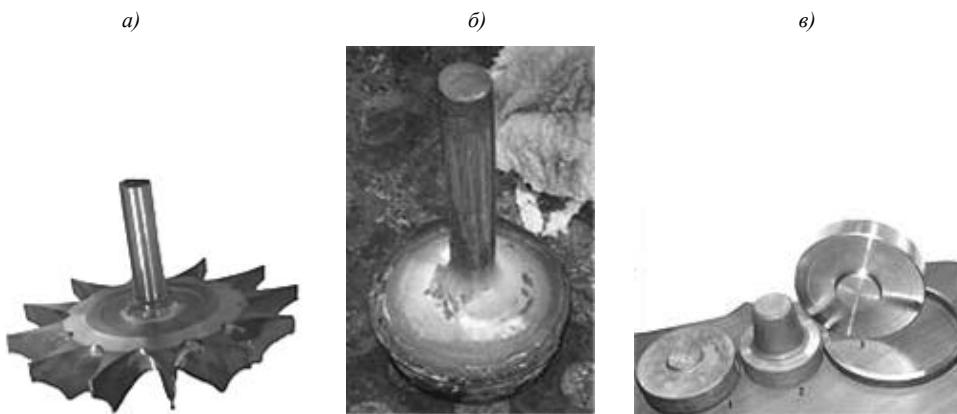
Изделия и заготовки из сплава ЭП975-ИД:
